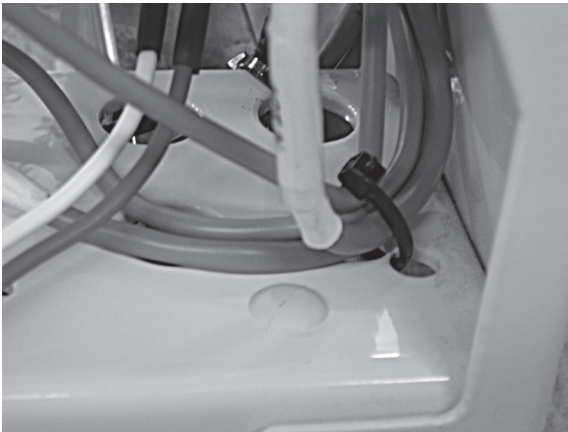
Mit einem Kabelbinder am Gehäuse fixierte Kabel
